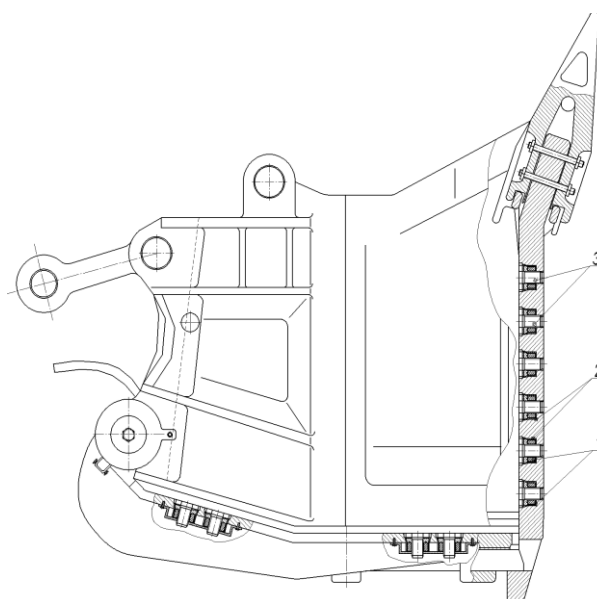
Ковш экскаватора с пьезокерамическими преобразователями
